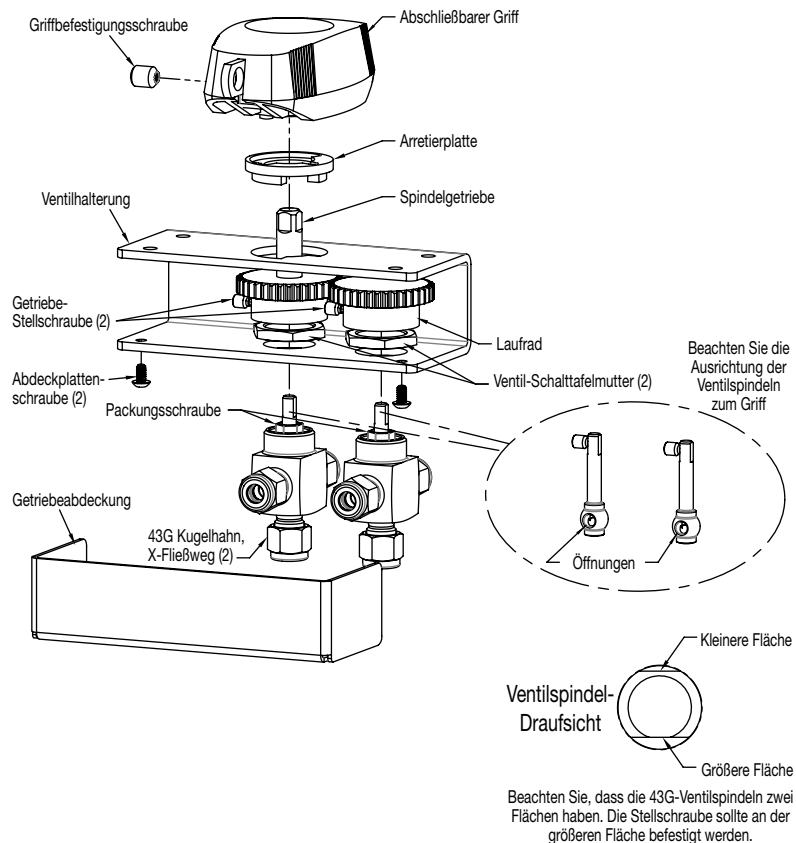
2-Ventil-GSM-Baugruppe Explosionsdarstellung
